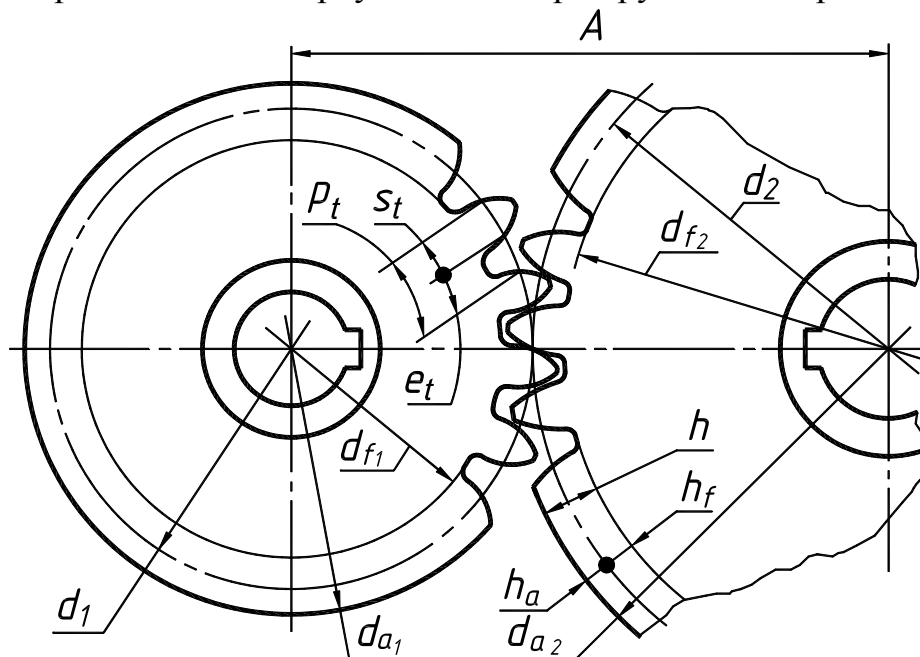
Геометрические параметры цилиндрической зубчатой передачи
